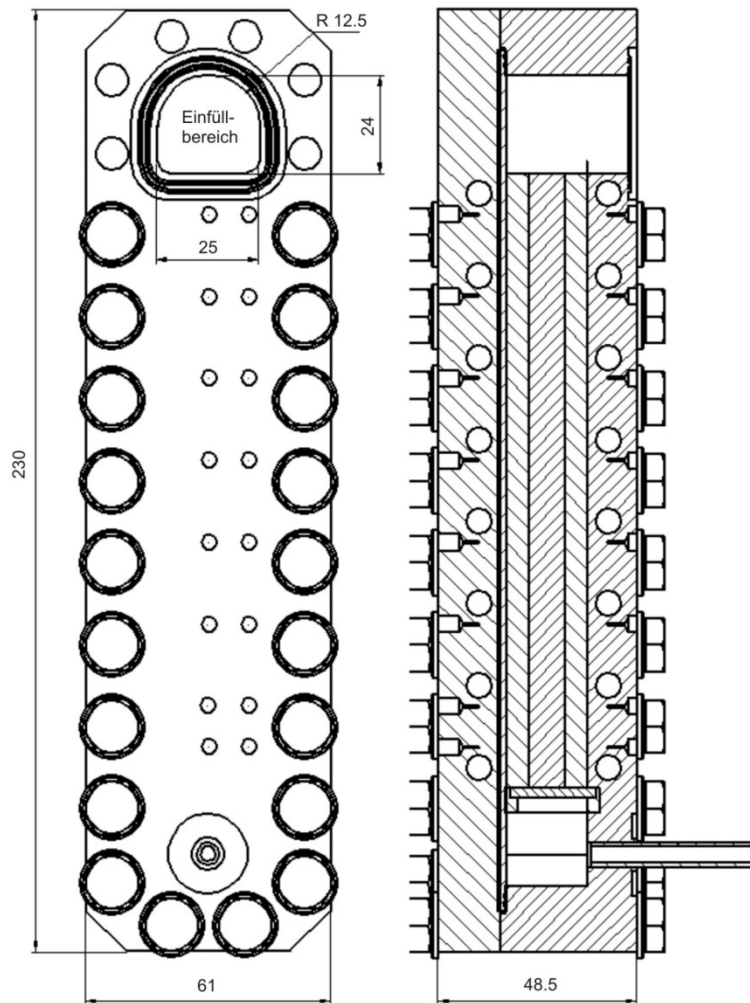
CAD (Frontalansicht und Schnitt) vom Reaktor inkl. Außenmaße in [mm].
